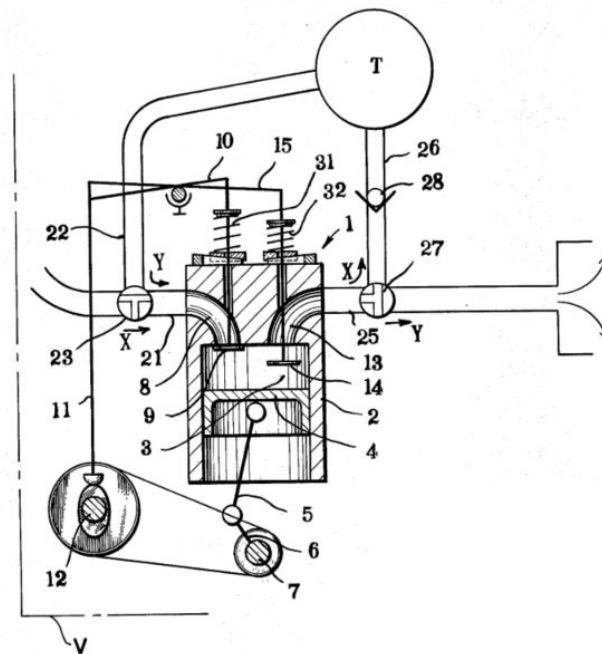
Motor convertível em compressor de ar e combustão interna, adaptado de [6].
